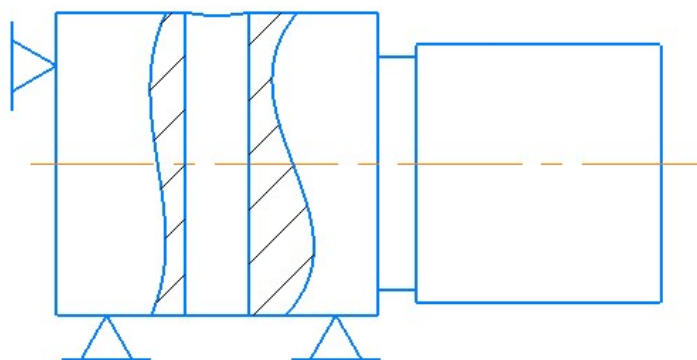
Базування поверхонь при свердлуванні отвору
